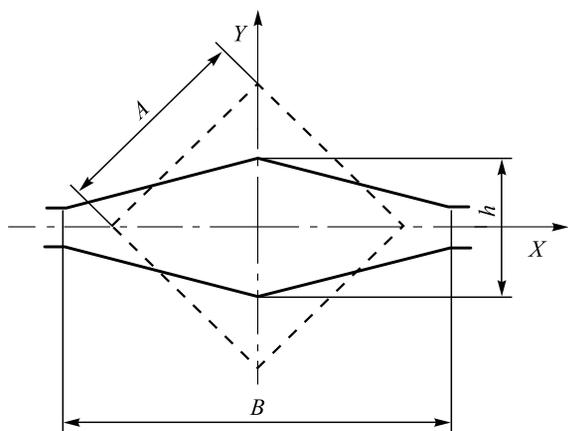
Схема вальцовки с калибровкой «повернутый квадрат – ромб»
